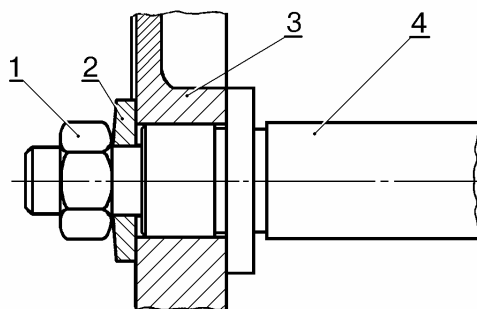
Крепление оси промежуточной шестерни заднего хода пятиступенчатой КП:
